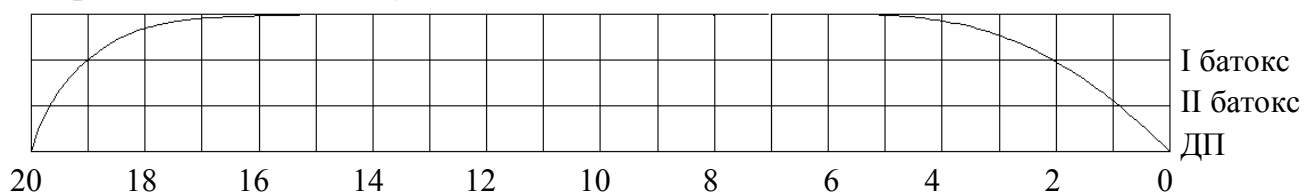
Фрагмент теоретичного креслення корпусу судна
